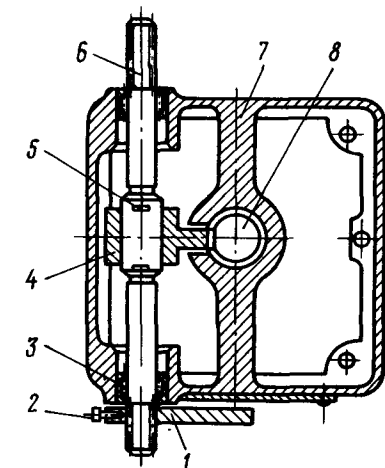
Верхний корпус регулятора: 1 — стрелка; 2 — винт; 3 — подшипник игольчатый; 4 — зубчатый сектор; 5 — шплинт; 6 — шлицевой валик; 7 — корпус; 8 — валик-рейка
